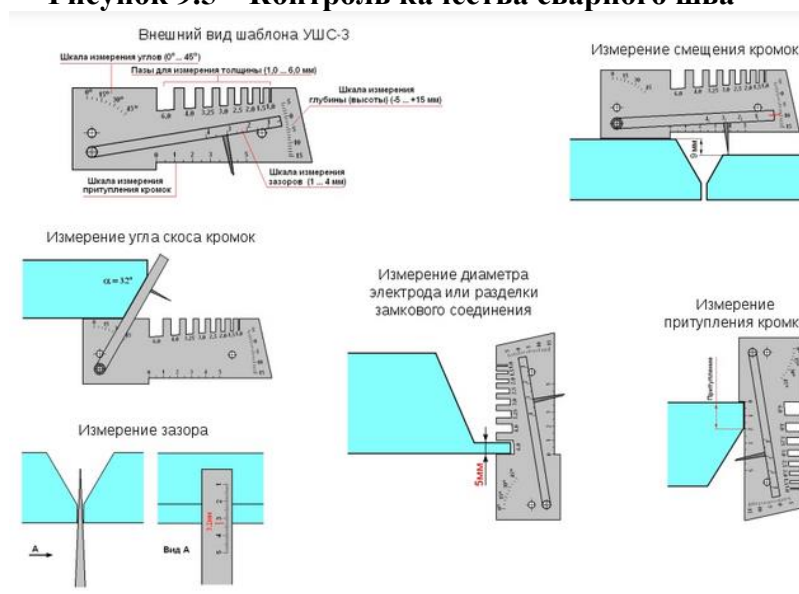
Измерительный контроль сборки и сварки
